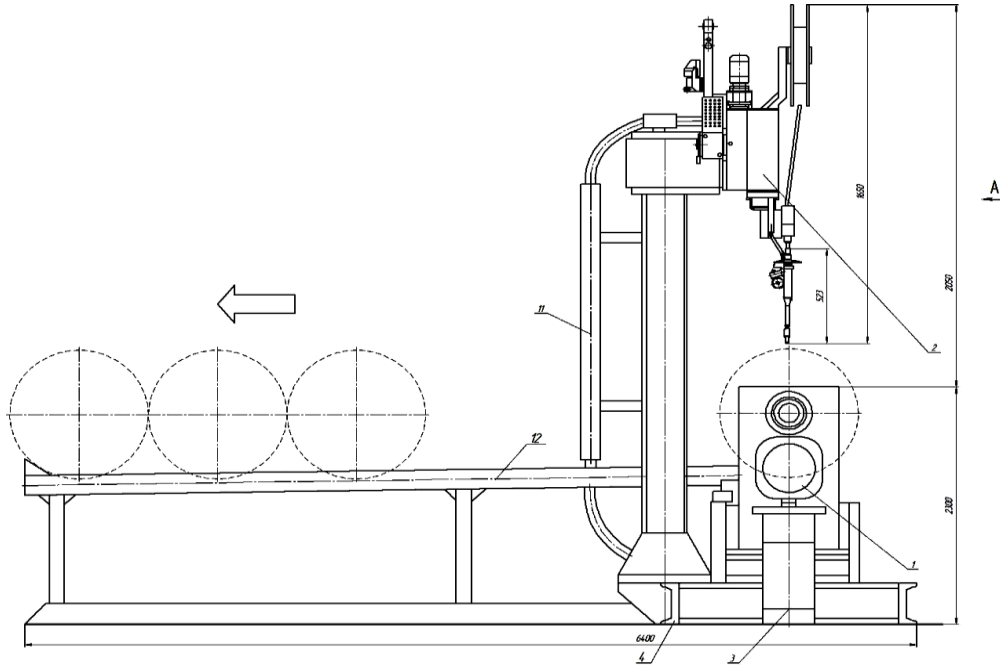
Загальний вигляд установки для складання і автоматичного зварювання обичайки ресивера із півсферичними днищами
